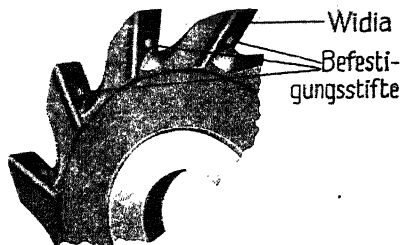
Befestigung von Widiaformstücken mittels Stiften in einem Fräser.
